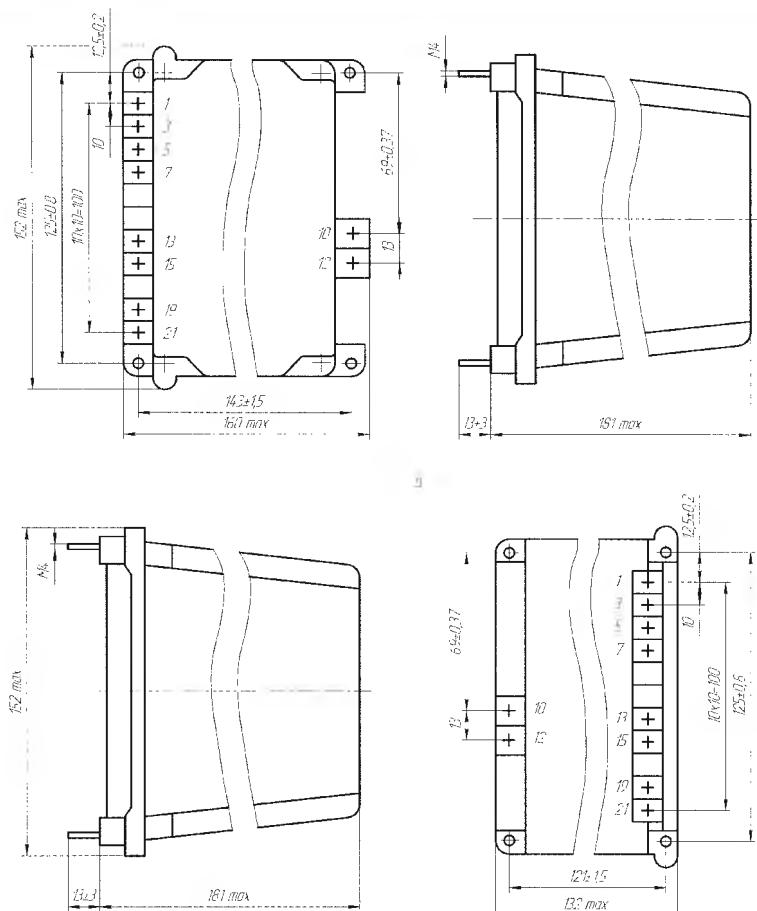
Габаритные, установочные и присоединительные размеры реле PCM 13.
